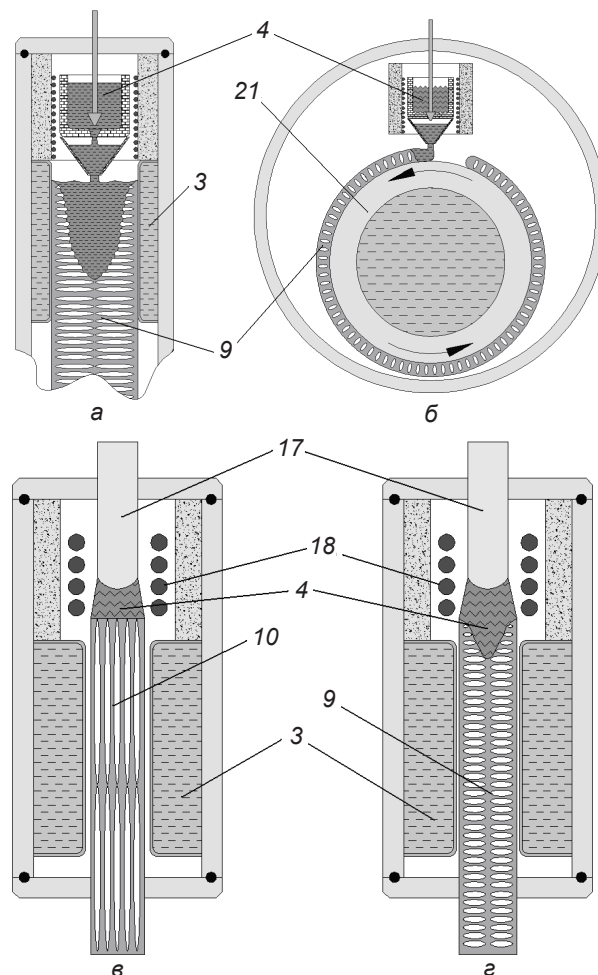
Схемы газар-установок для получения газов непрерывным методом: а – заливка внутрь неподвижного кристаллизатора и вытягивание слитка вниз; б – заливка на поверхность вращающегося водоохлаждаемого цилиндра; в – переплавка монолитного стержня внутри кольцевого индуктора с получением параллельных пор (стержень и газар движутся вниз); г – переплавка монолитного стержня внутри кольцевого индуктора с получением радиальных пор (стержень и газар движутся вниз); 17 – базовый материал в виде монолитного стержня или трубы; 18 – кольцевой индуктор; 21 – водоохлаждаемый вращающийся кристаллизатор
